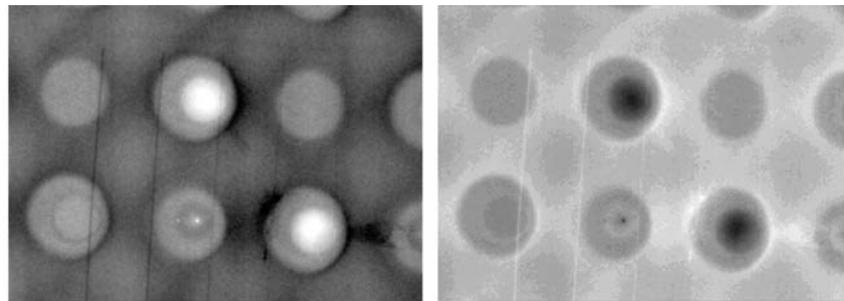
Цифровые изображения в семикратном увеличении дефектного участка образца с двойной точечной сваркой, полученные с применением твердотельного преобразователя типа S10811-11: а – негатив; б – позитив
